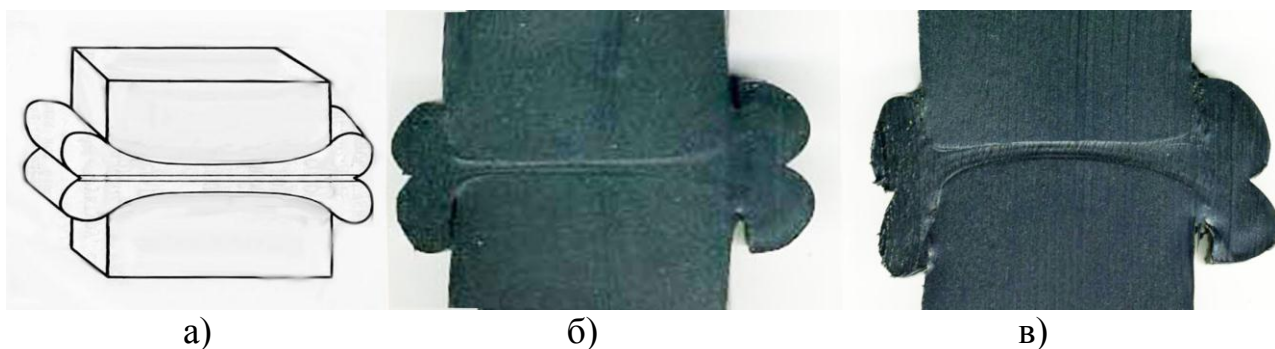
Перераспределение расплава при сварке труб с вертикальным расположением осей
